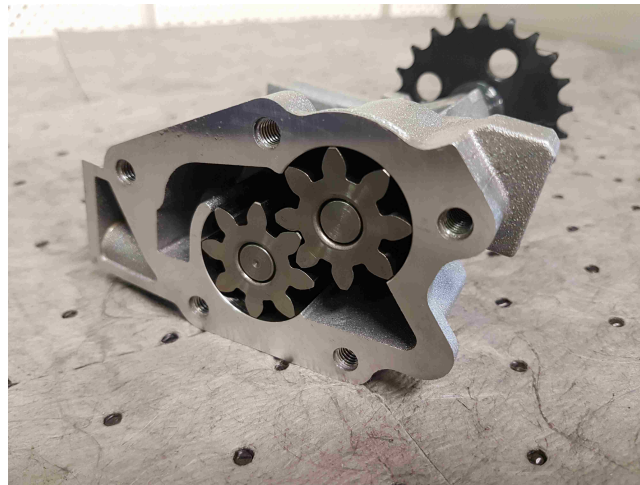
Bomba de óleo de engrenagem externa, de cilindrada fixa.
